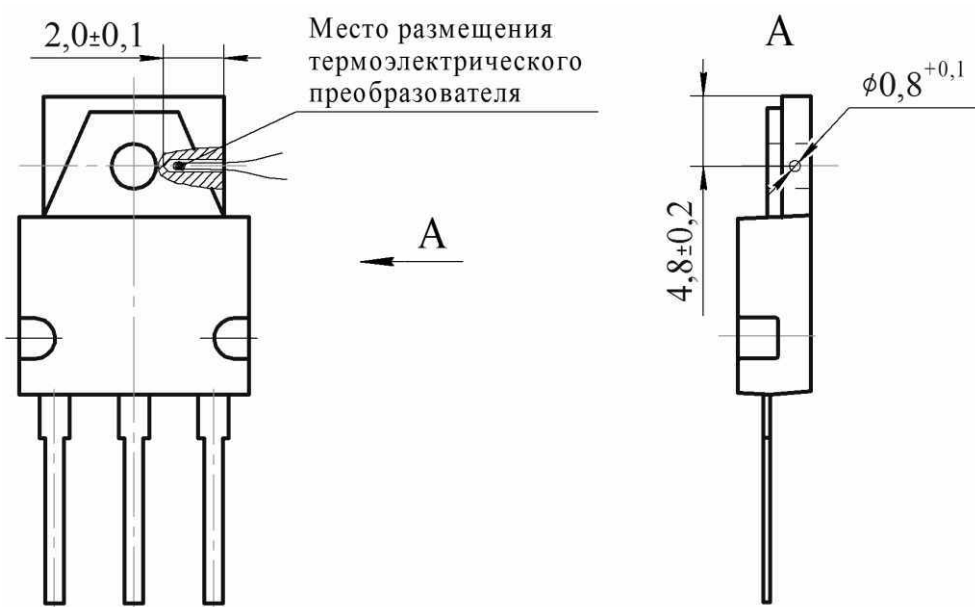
Место размещения термоэлектрического преобразователя для контроля температуры корпуса сборок в корпусе КТ-43В
